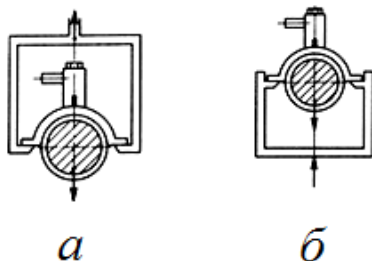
Схемы испытания седлового отвода на отрыв:
